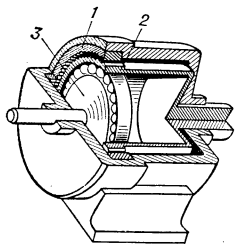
Зубчатая волновая передача (редуктор): 1 — жёсткое колесо; 2 — гибкое колесо; 3 — генератор волн.
